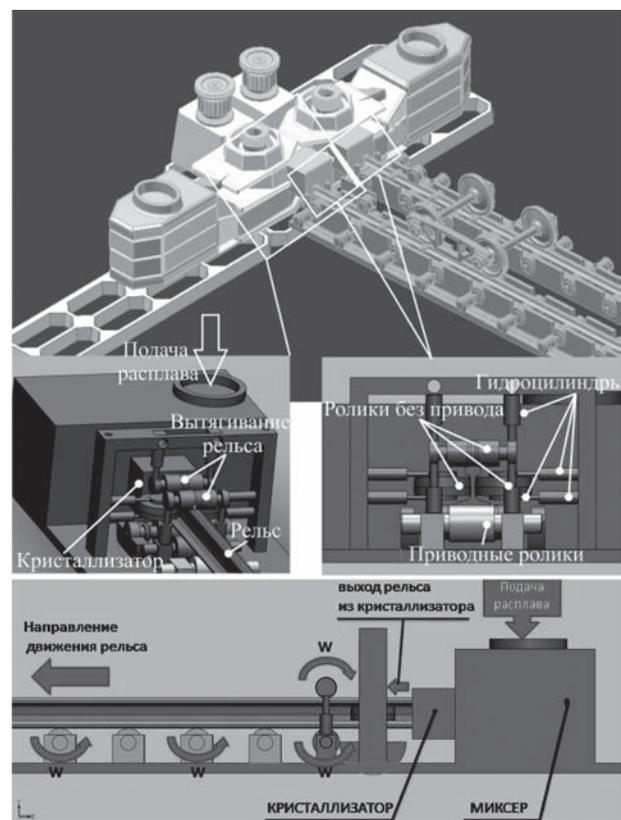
Схема установки для непрерывной отливки чугунных рельсов
